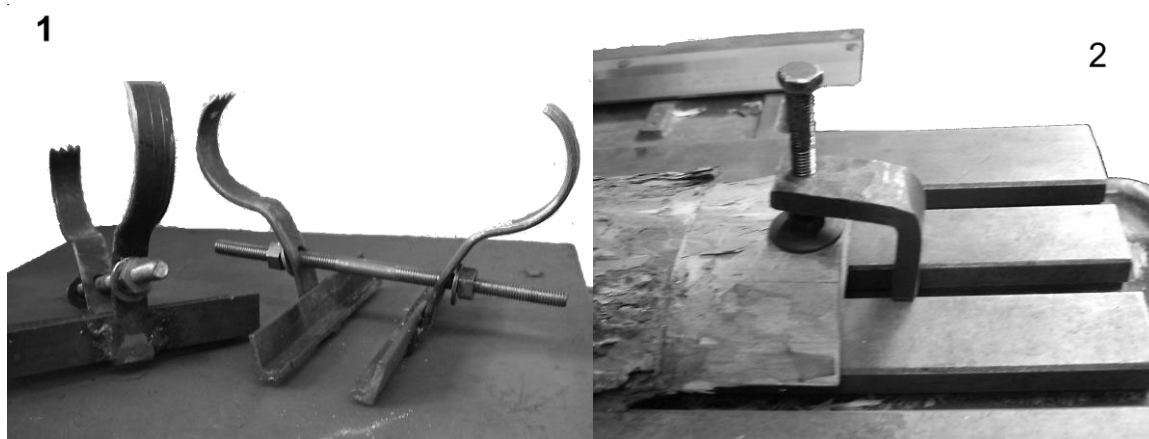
Приспособления (струбцины) для закрепления образцов 1 - круглого сечения; 2 – пиломатериалов.
